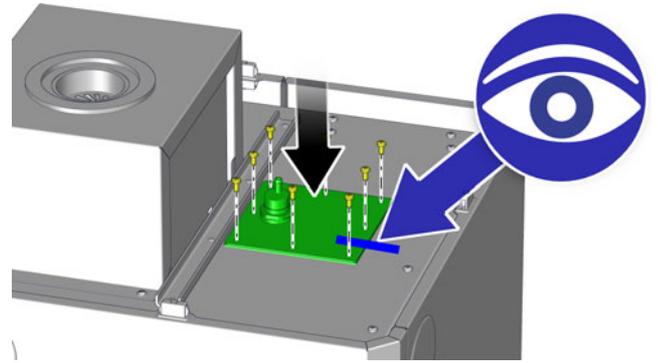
Tôle de montage du capteur de niveau de remplissage
